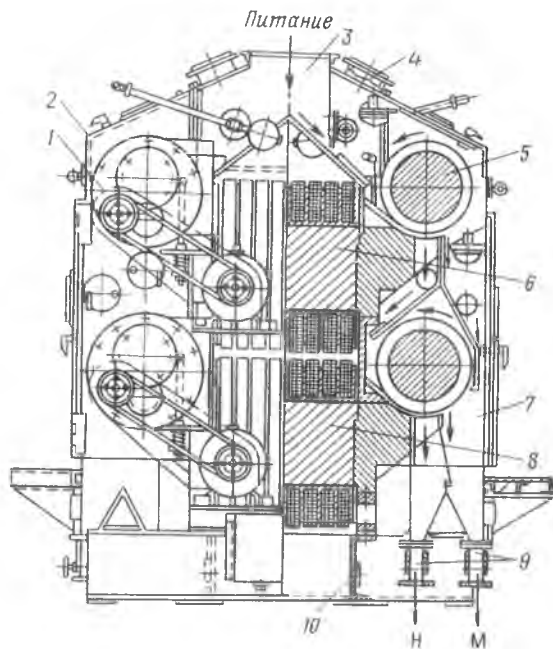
Электромагнитный валковый сепаратор 4ЭВС-36/100;
